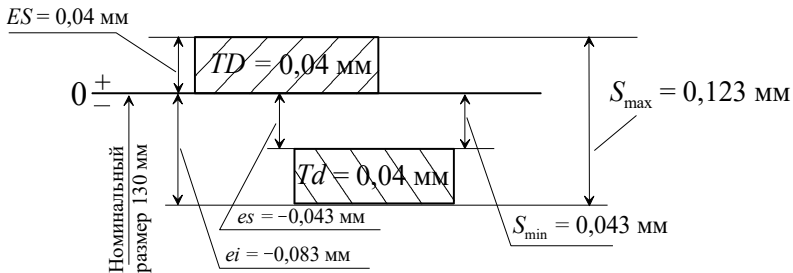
Схема расположения допусков соединения 1
